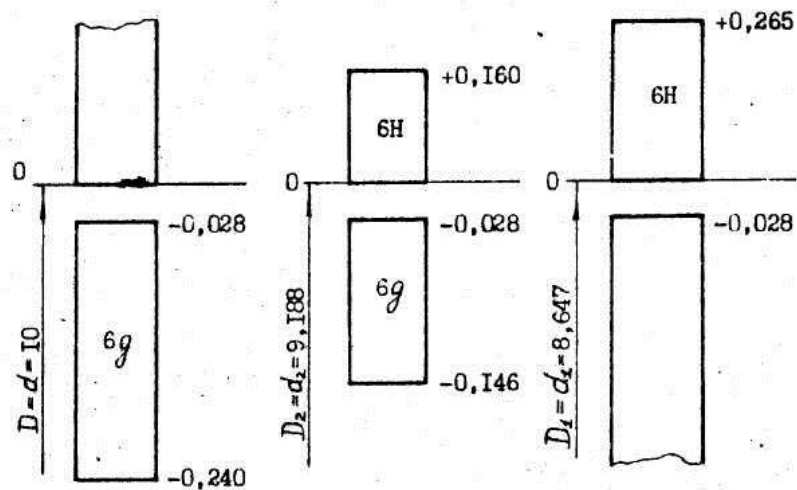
Схеми розташування полів допусків деталей різьбового з'єднання $M10 \times 1,25-6H/6g$ по зовнішньому, середньому і внутрішньому діаметрам
